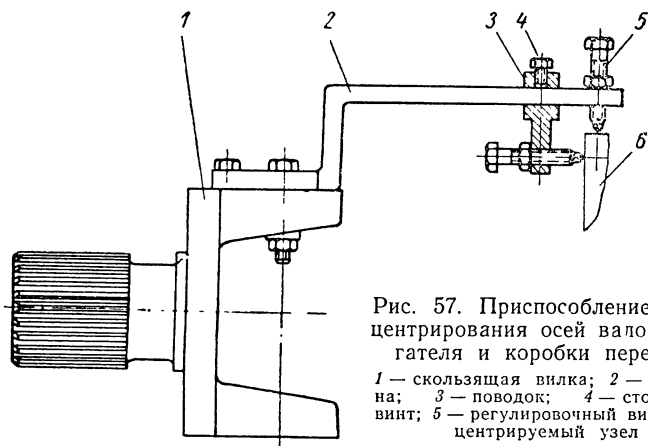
Приспособление для центрирования осей валов двигателя и коробки передач:
